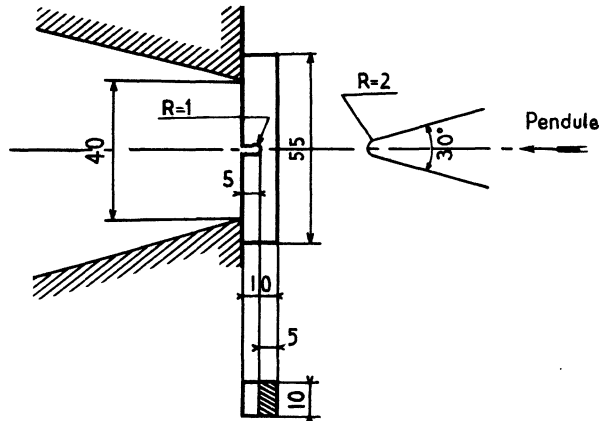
Vue de dessus d'une éprouvette calée contre son support (dimensions en mm)
